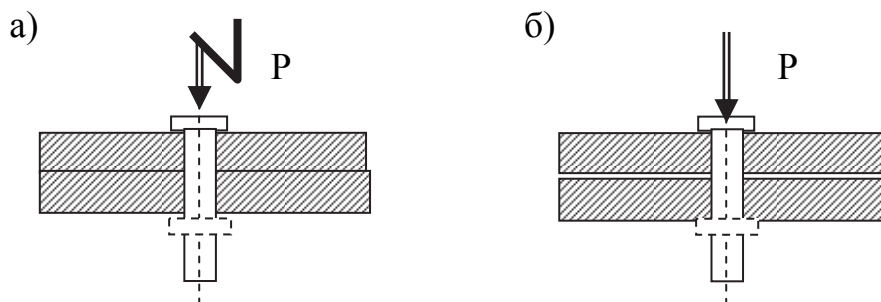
Схемы клепки: а – ударной; б – прессовой
